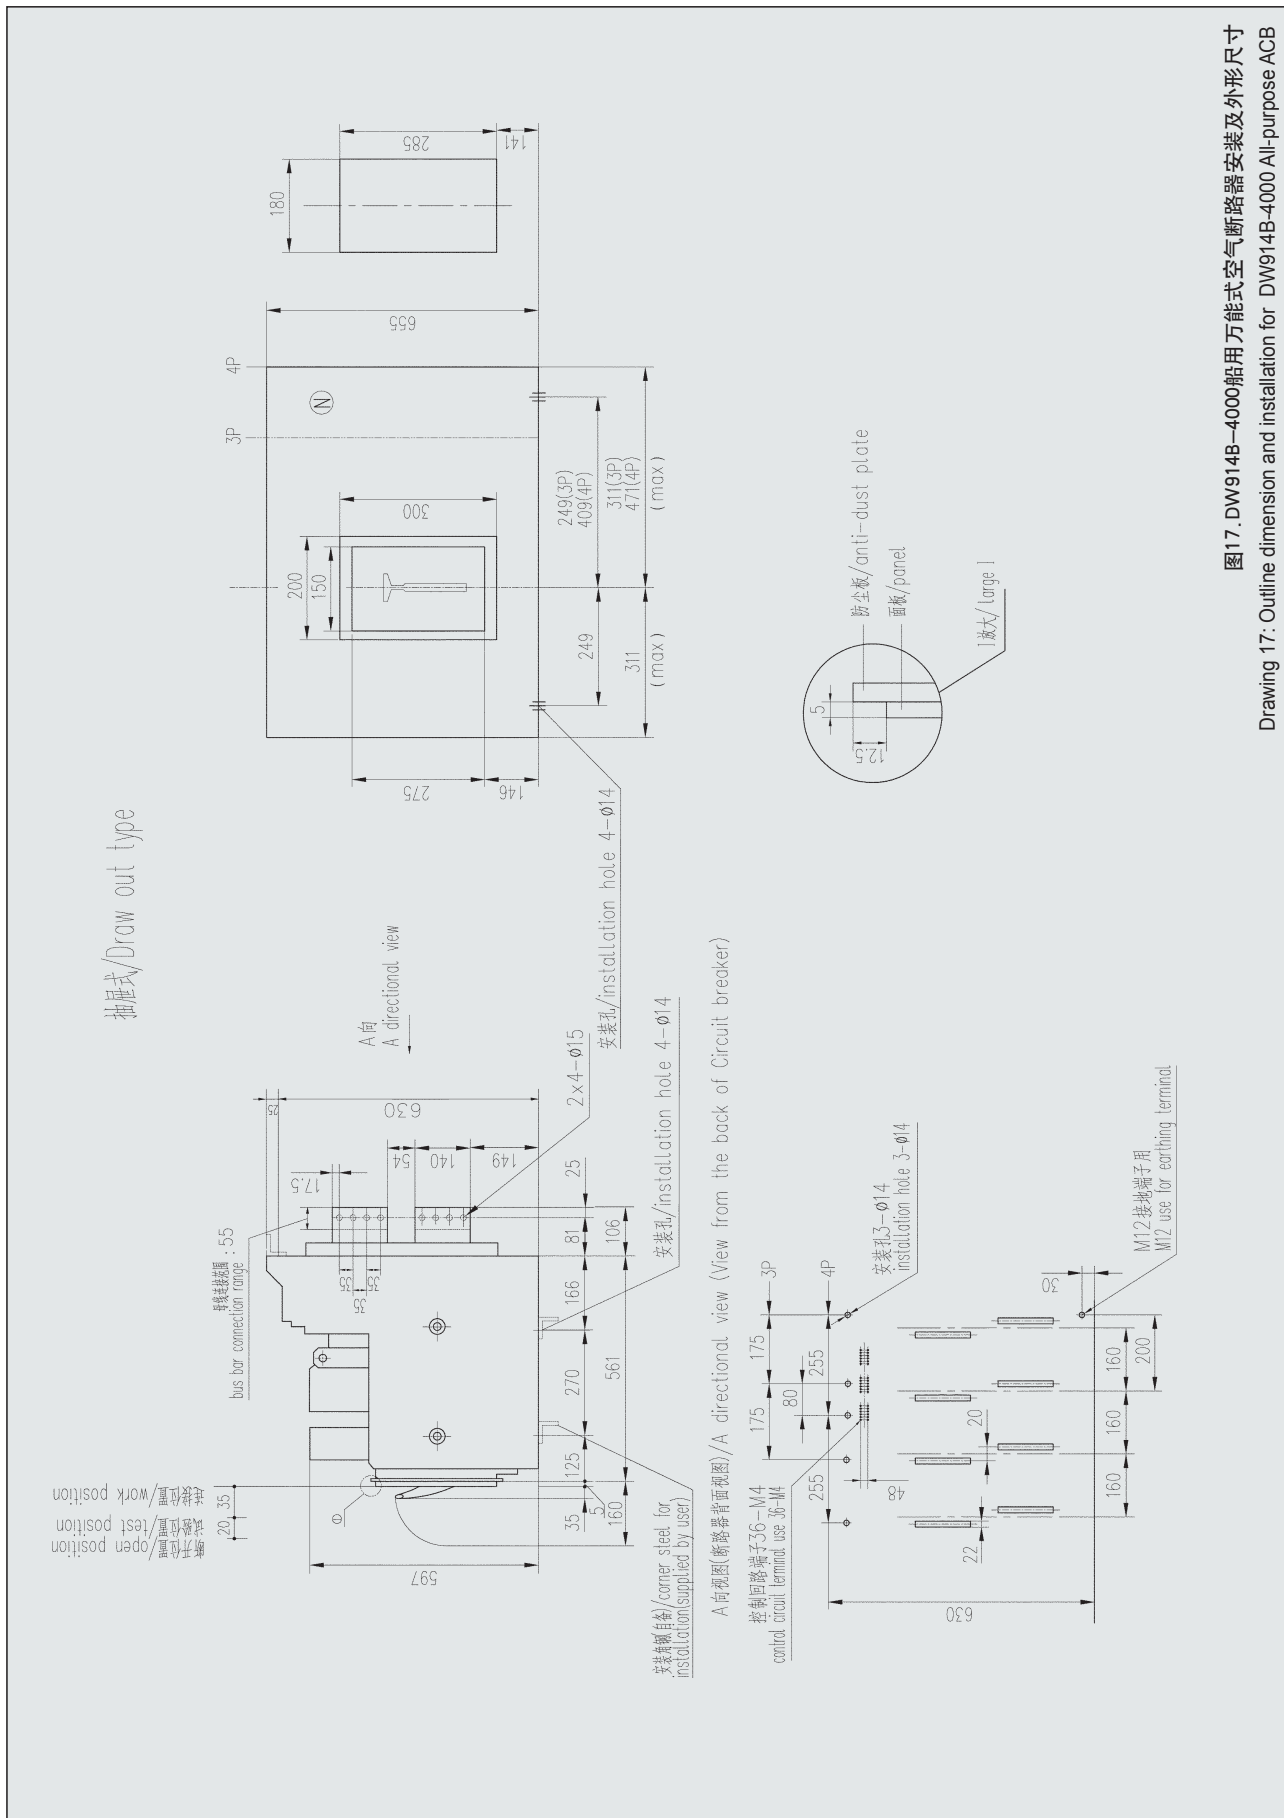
DW914B-4000船用万能式空气断路器安装及外形尺寸
